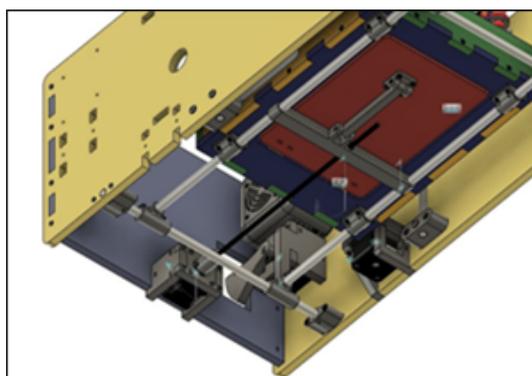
Печатный станок для слабовидящих (вид снизу)
